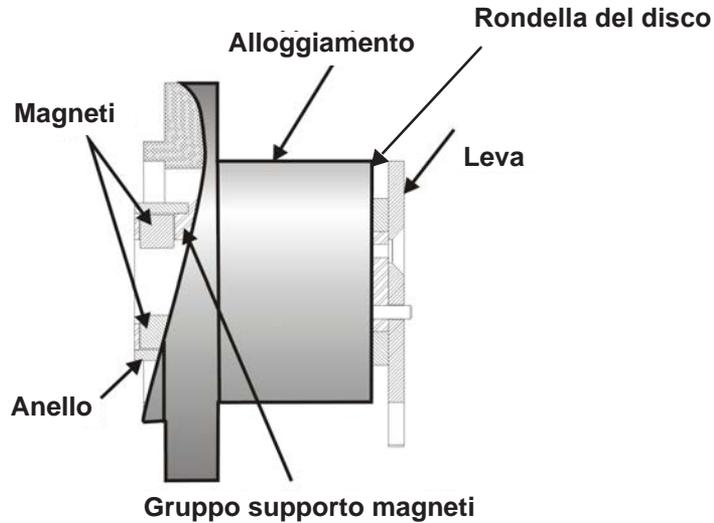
Supporto magneti sulla valvola a movimento alternato
